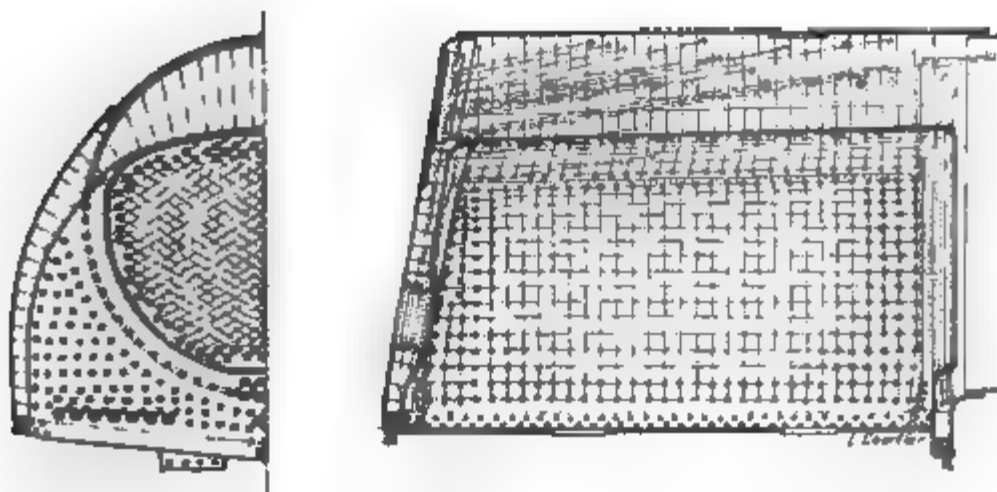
Foyer Wooten pour locomotive à anthracite type 2-8-0 du D. & H.
